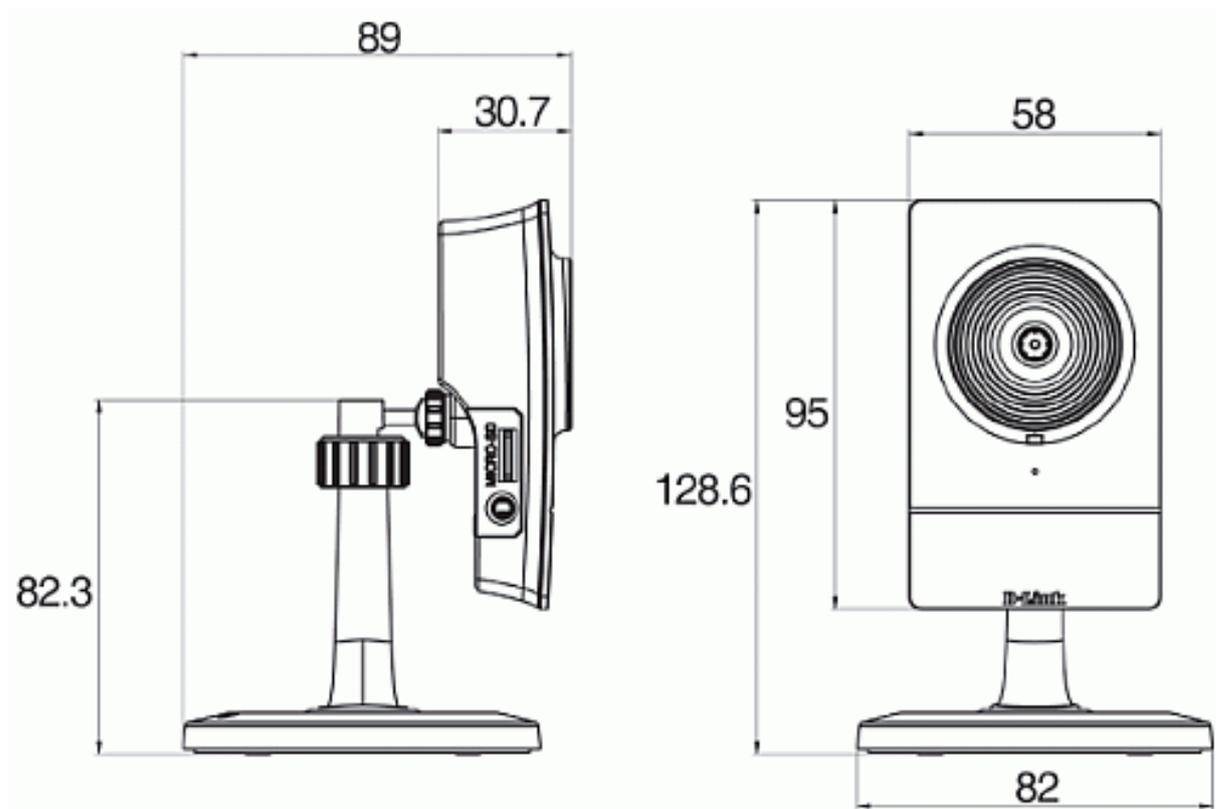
Габаритные размеры камеры D-Link DCS-2103 [12]
